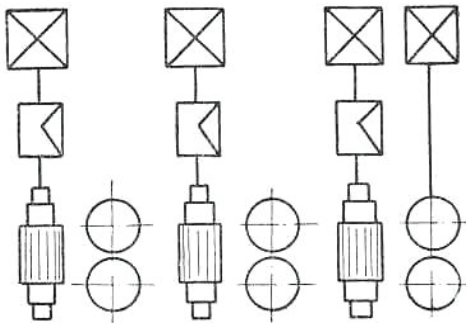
Схема непрерывно-заготовочного стана с неприводными клетями
